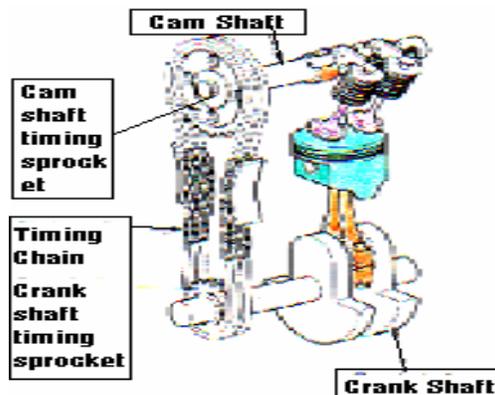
Mekanisme katup tipe Double Over Head Cam shaft (DOHC)
